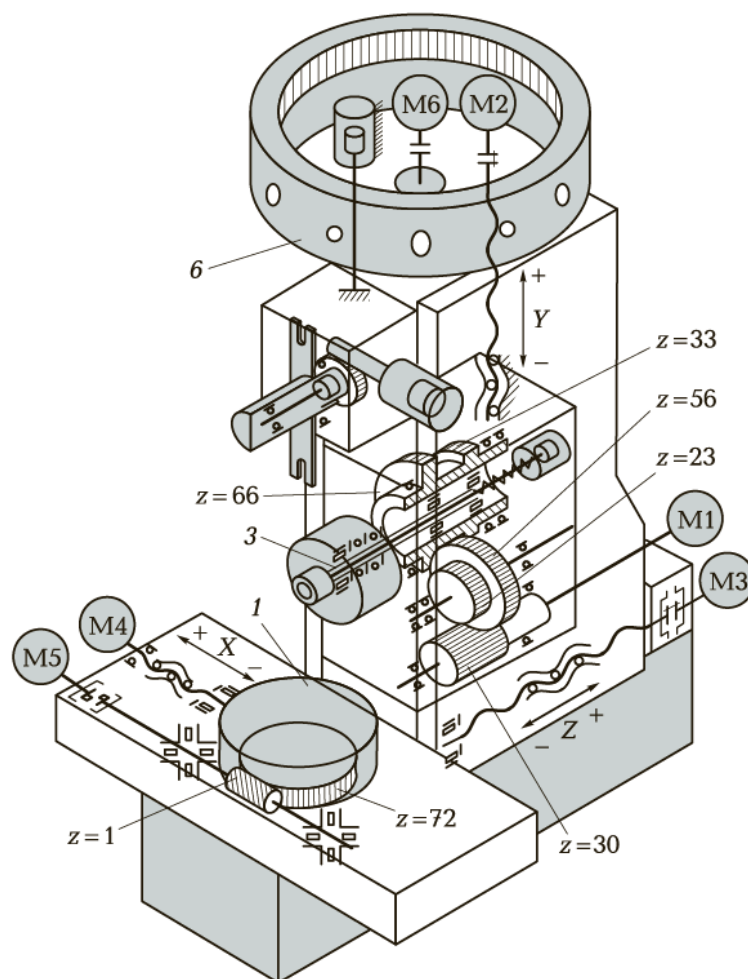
Кінематична схема горизонтального обробного центру з ЧПК для обробки корпусних деталей мод. ІР500ПМФ4
